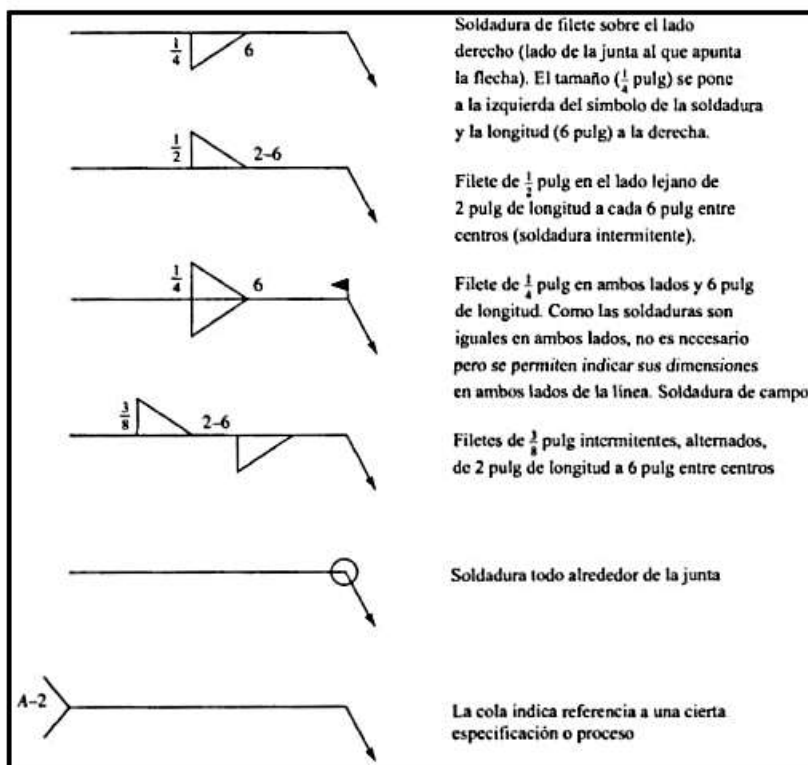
EJEMPLOS DE SOLDADURAS⁴⁴
